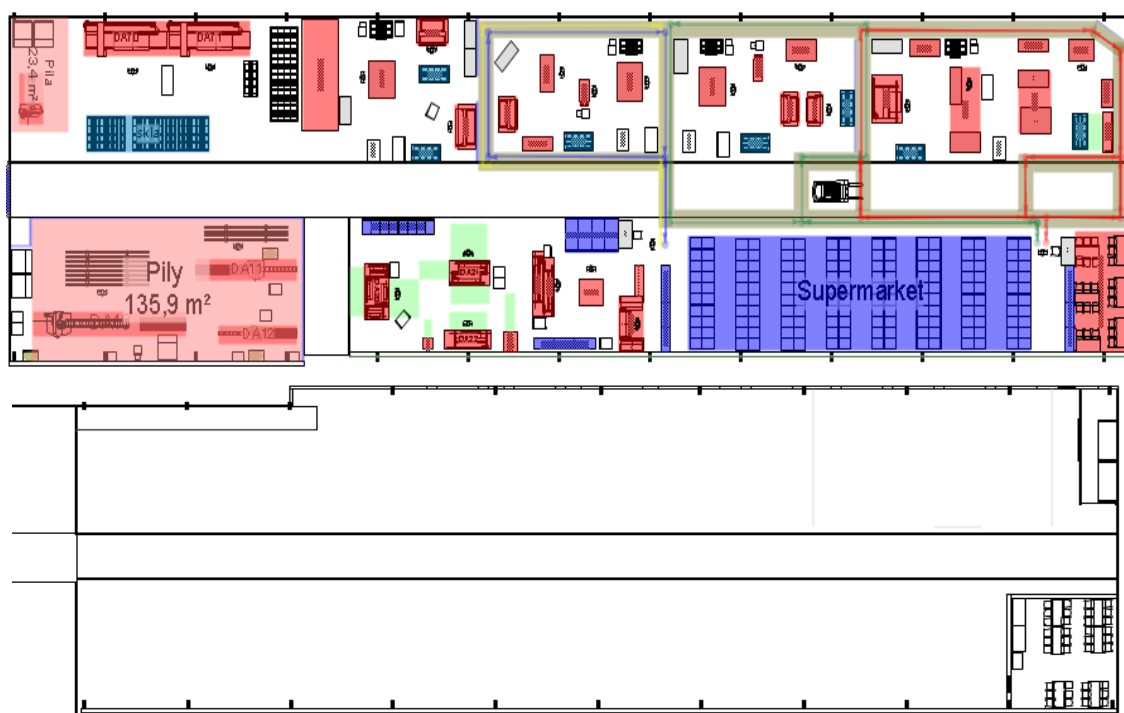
2D layout výrobní buňky pro žlutý montážní tým s vyznačenými drahami
